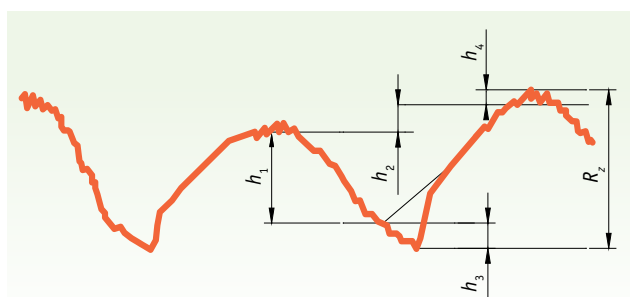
Схема для расчета высоты профиля шероховатости поверхности при точении:  $h_1, h_2, h_3, h_4$  — составляющие шероховатости
